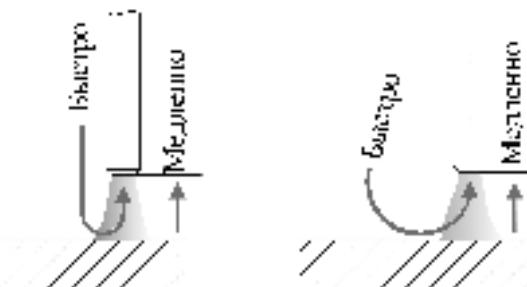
Способы зажигания сварочной дуги.
